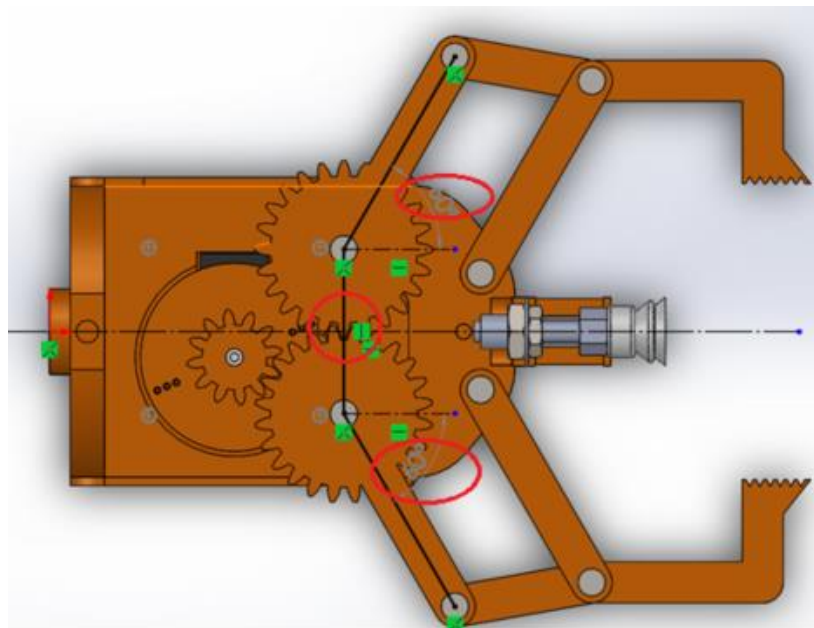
26. Detalle acoplamiento entre engranajes del sistema pinza
